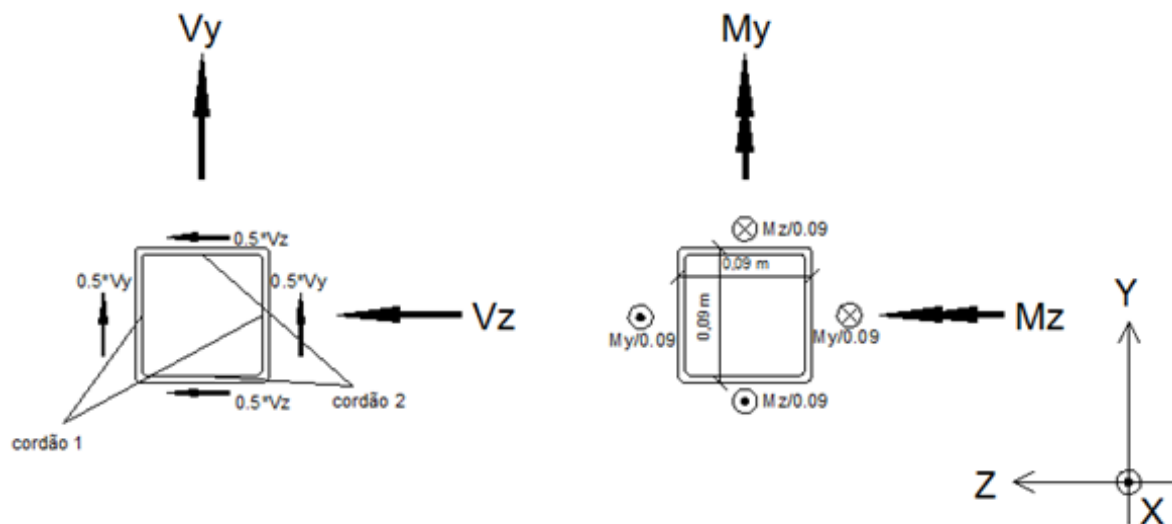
Modelo de cálculo para o dimensionamento do cordão de soldadura, parte 2
